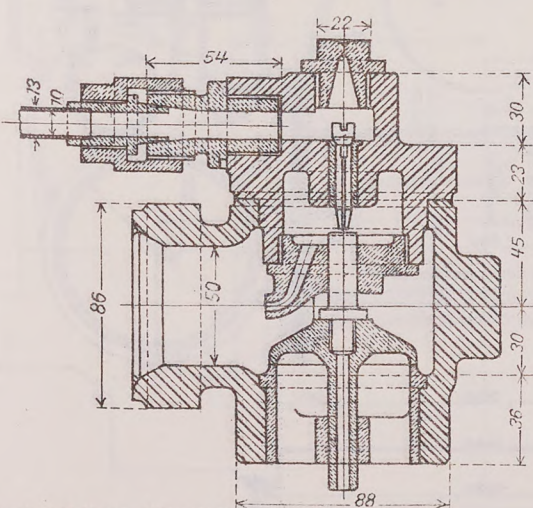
bis 12. Ventil einer Öltriebmaschine.
